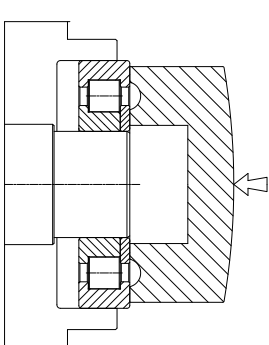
Montaggio albero-sede Mounting on shaft-seating
